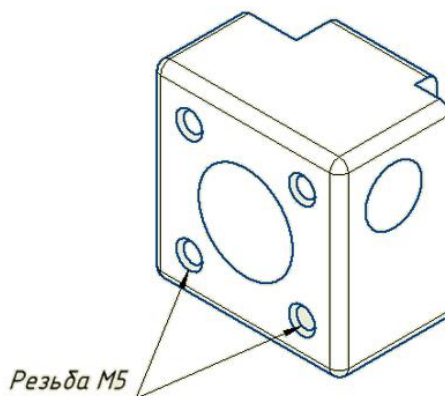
Корпусная деталь с одинаковыми резьбовыми отверстиями
